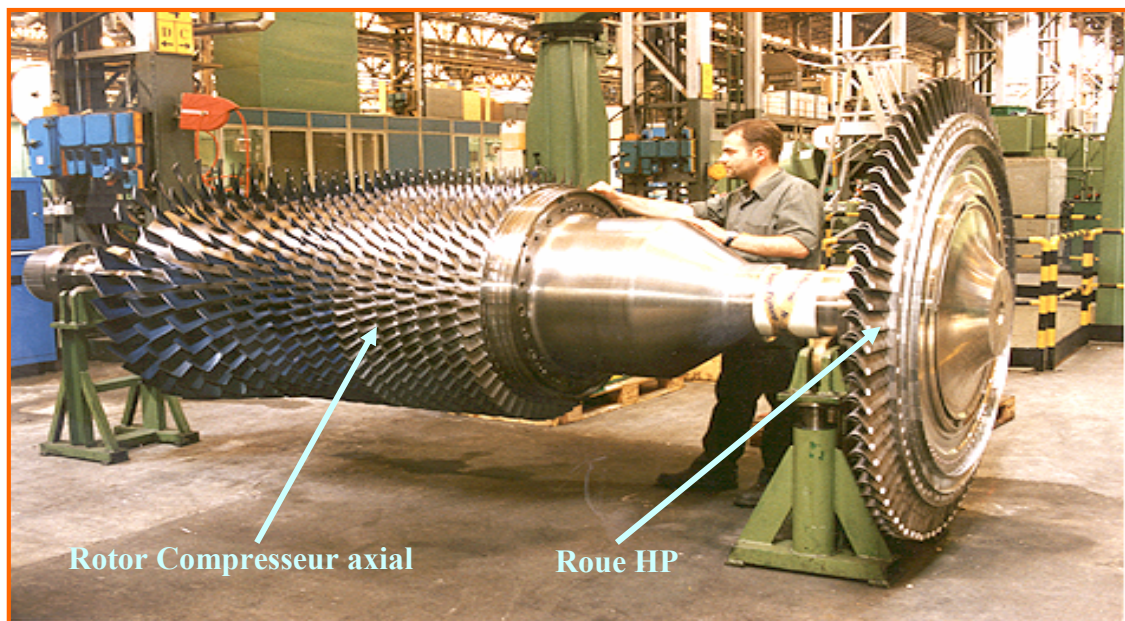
Rotor du Compresseur de la turbine à gaz MS 5002C.
